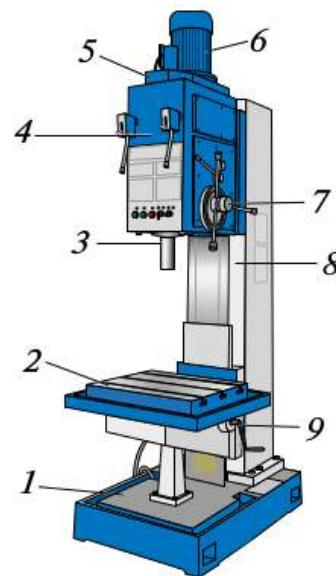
Вертикально-сверлильный станок напольного типа:
